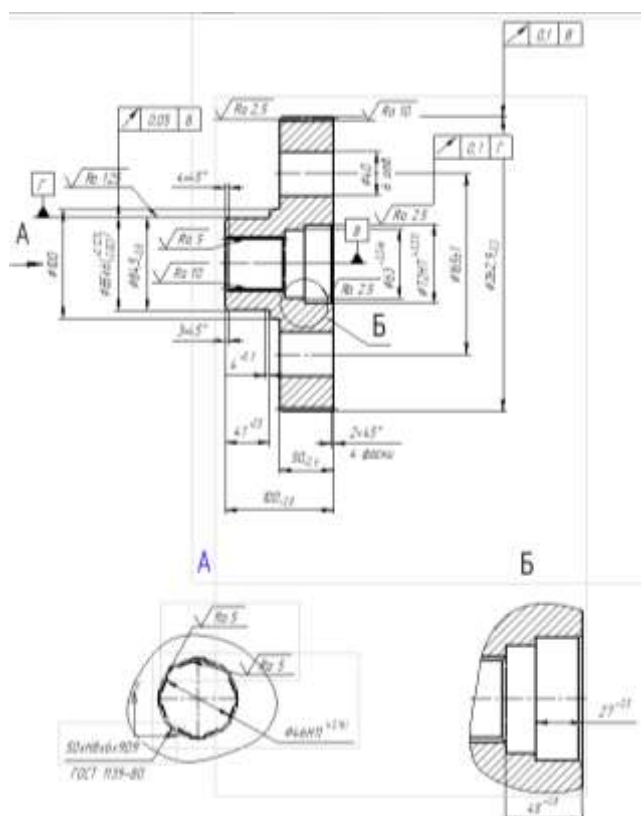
Эскиз детали «Колесо зубчатое механизма поворота»
